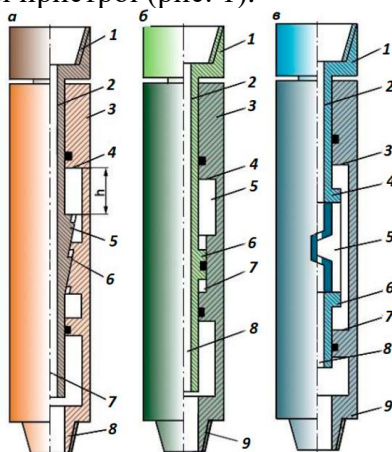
Ударні механізми: *a* – ВУК: 1 – верхнє з'єднання; 2 – ствол; 3 – корпус; 4 – ковадло; 5 – бойок; 6 – замок; 7 – канал для бурового розчину; 8 – нижнє з'єднання; *б* – ГУМ (вказано лише змінєні позиції): 5 – камера великого діаметру; 6 – поршень-бойок; 7 – камера малого діаметру; 8 – канал; 9 – нижнє з'єднання; *в* – УЛП: 3 – верхнє ковадло; 4 – верхня частина бойка; 5 – замок; 6 – нижня частина бойка; 7 – нижнє ковадло; 8 – канал
